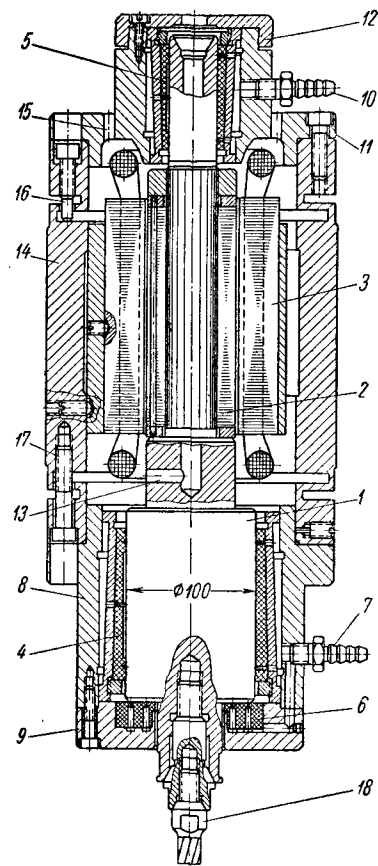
Фрезерная головка на опорах с воздушной смазкой
